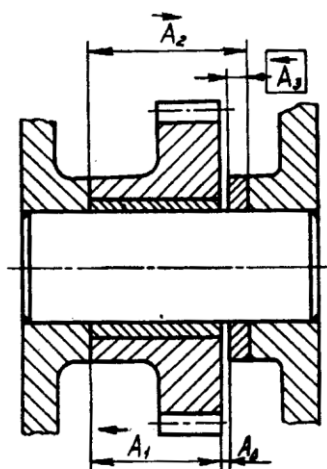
Размерная цепь на определении зазора между зубчатым колесом и торцом проставочного кольца
